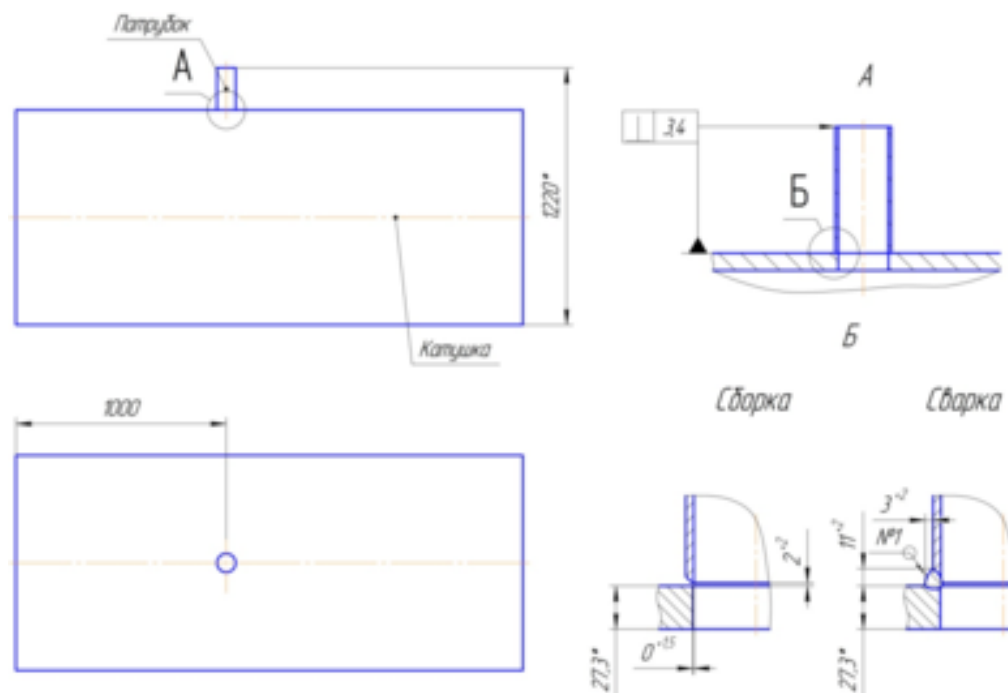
Схема сборки и сварки патрубка с катушкой
